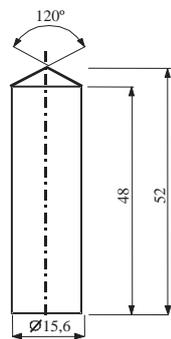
Piston cylindrique en bronze, dimensions en mm
